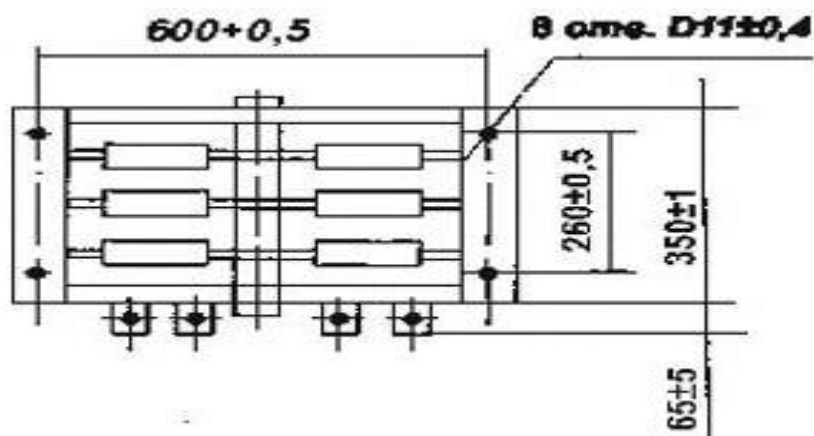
Общий вид, габаритные и установочные размеры блоков и схема размещения резисторов в блоке.
